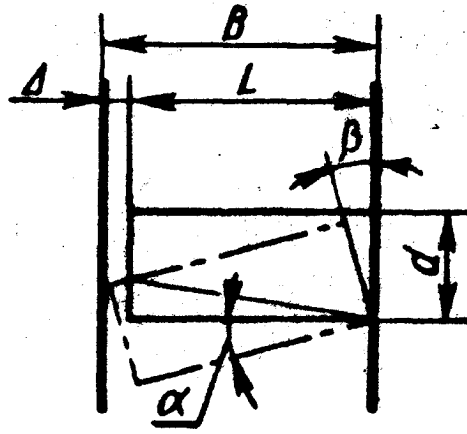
Схема для расчета проходимости заготовок (деталей) в коробчатых лотках
